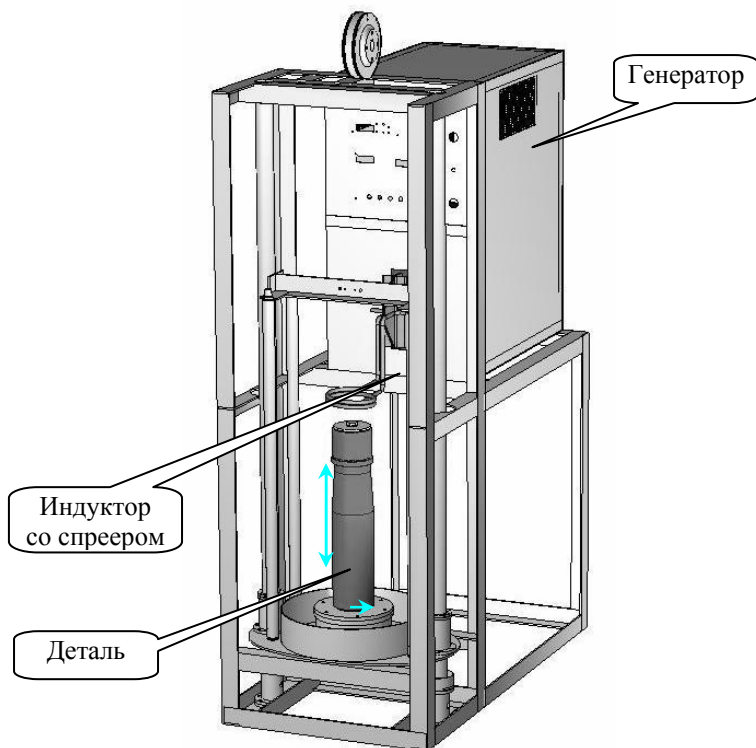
Внешний вид станка – полуавтомата для поверхностной заделки
